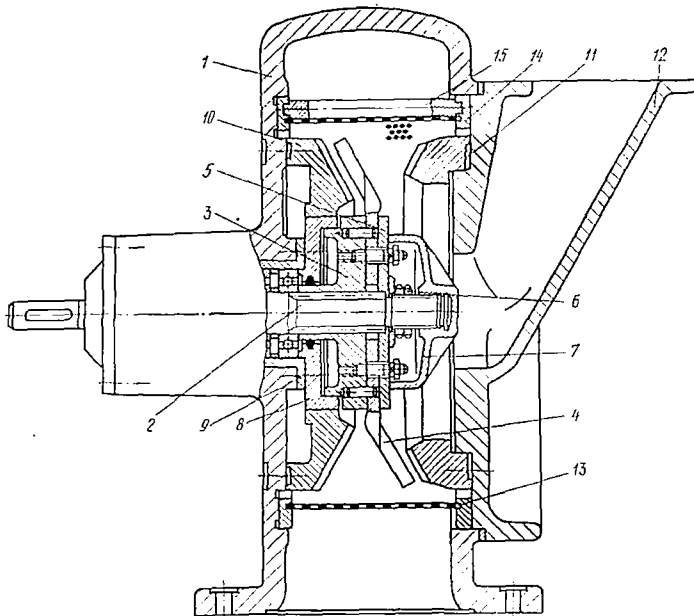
Зубчатая дробилка для измельчения отходов реактопластов
